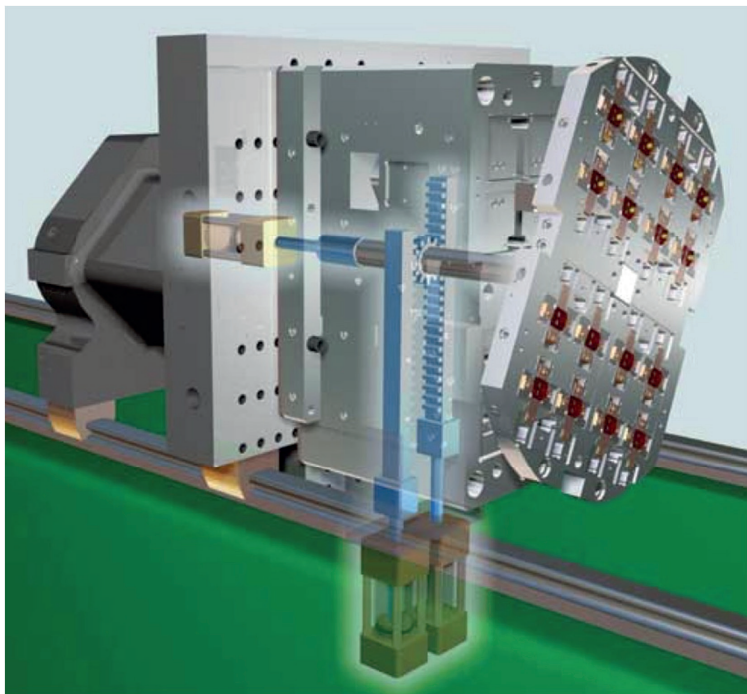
Příklad formy s rotací kolem svislé osy
